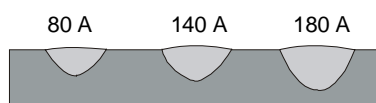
Penetração de solda em função da corrente de soldagem.
